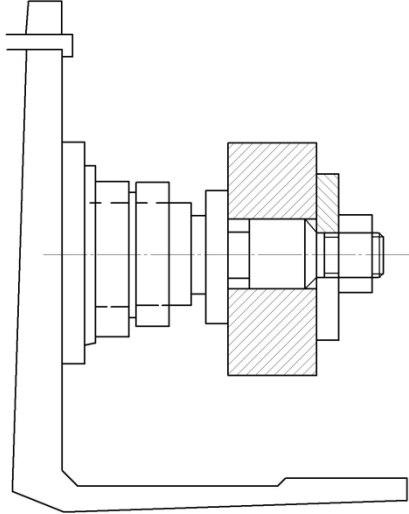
Консольная оправка для установки заготовки по отверстию с зазором
